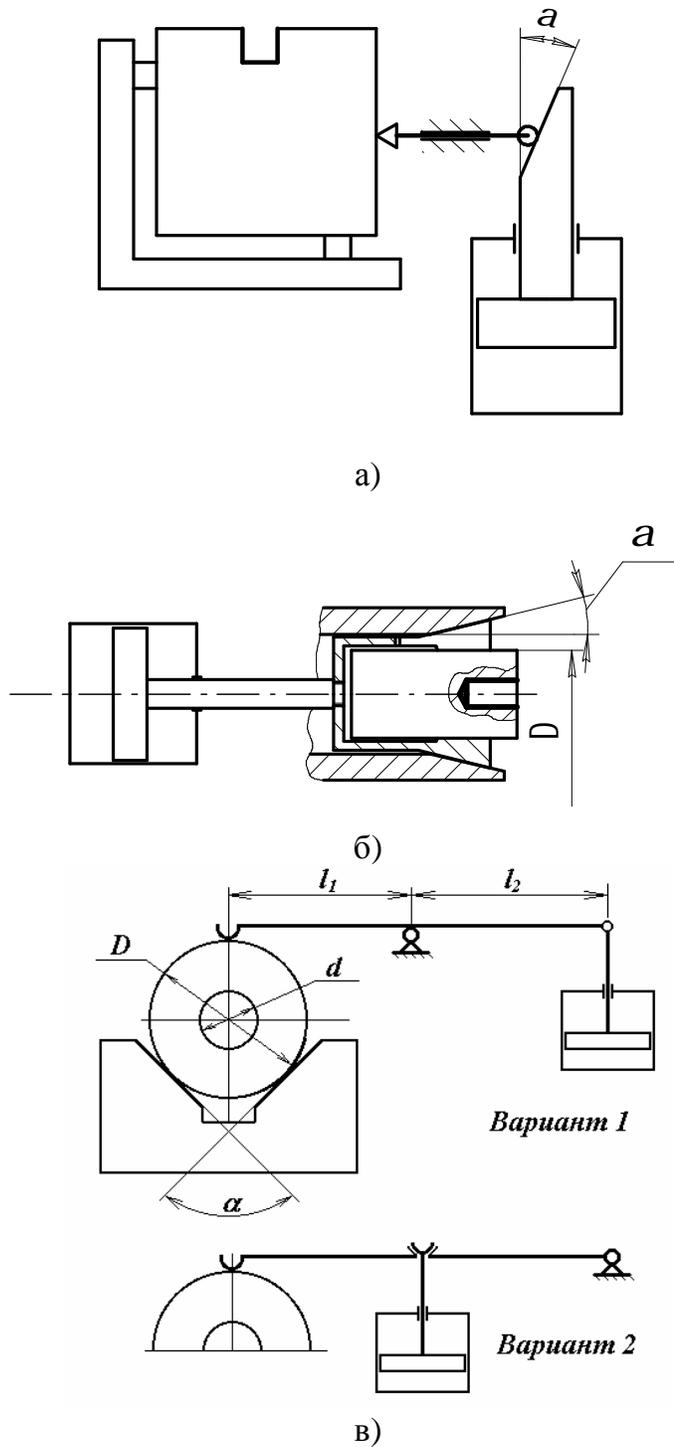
Принципиальные схемы приспособлений (а- для фрезерования паза; б – для сверления на токарном станке; в- для сверления отверстия на валу.)
